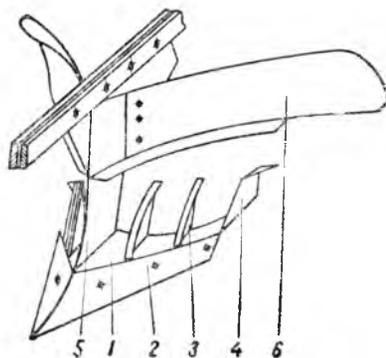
Схема просеивающего корпуса лесного плуга ИБЛ-56: 1 — плита; 2 — лемехи; 3 — просеивающие «решета»; 4 — подрезывающие «решета»; 5 — стойка; 6 — отвалы.
